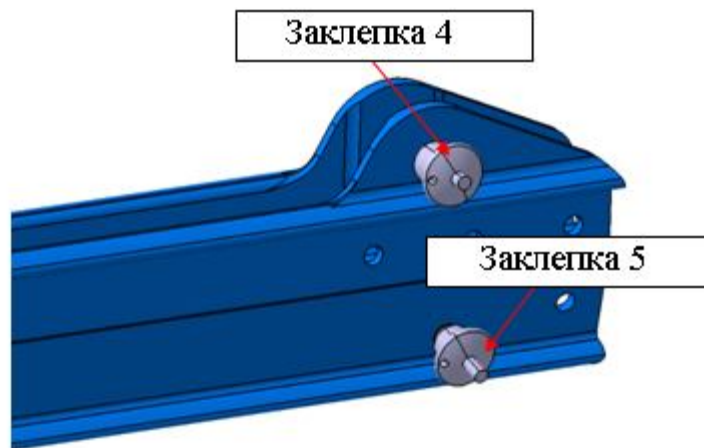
Головний вид 3D встановлення заклепок в рейках
